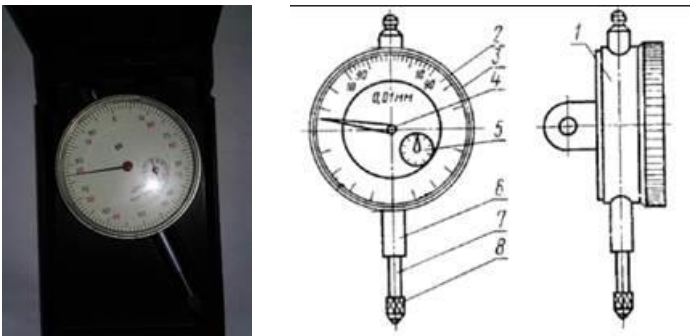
Загальний вигляд індикатора годинникового типу:
